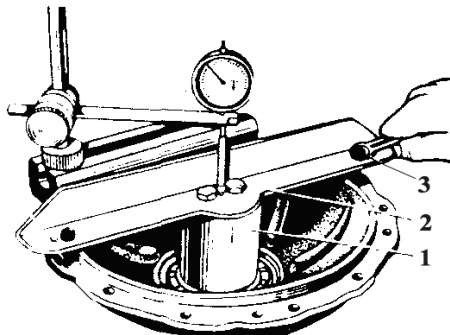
Проверка осевого зазора в подшипниках редуктора
